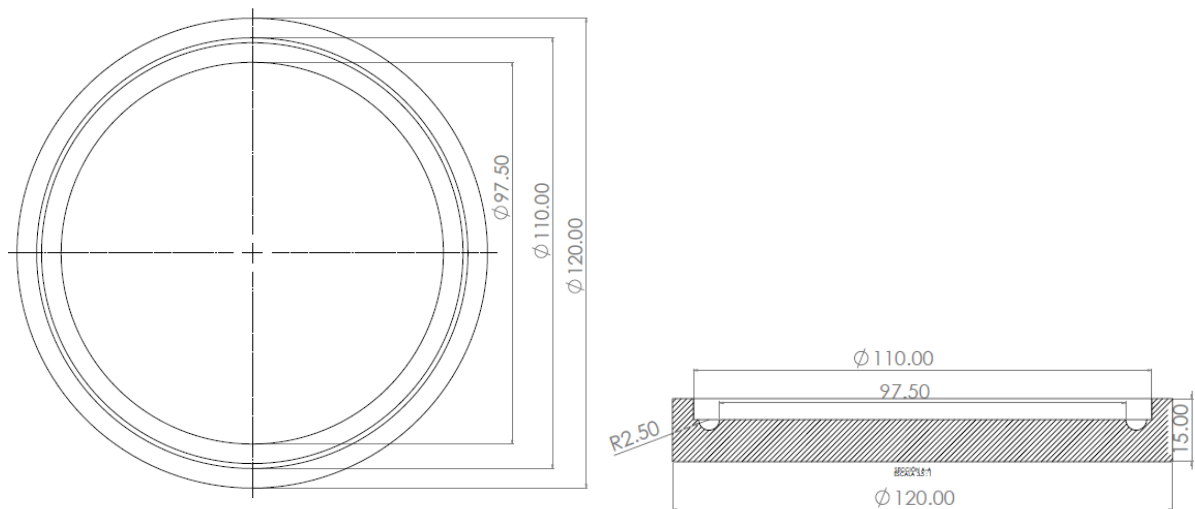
Tapa del sensor, vista planta y sección B-B]
